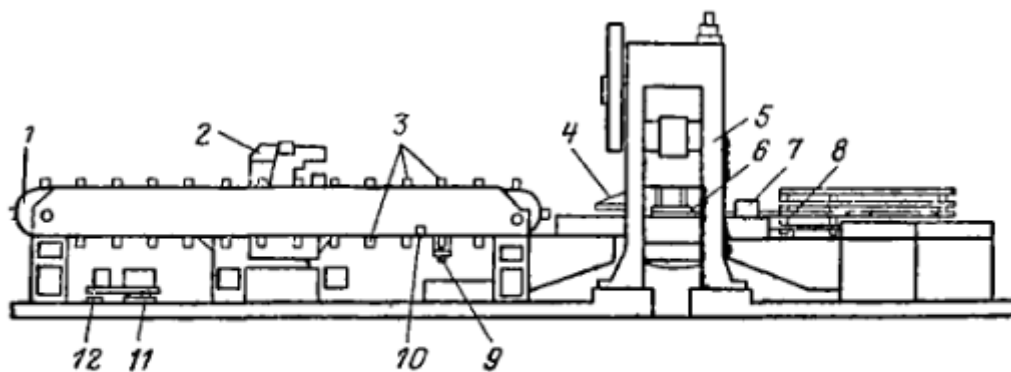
Автоматическая линия изготовления коллекторных пластин
